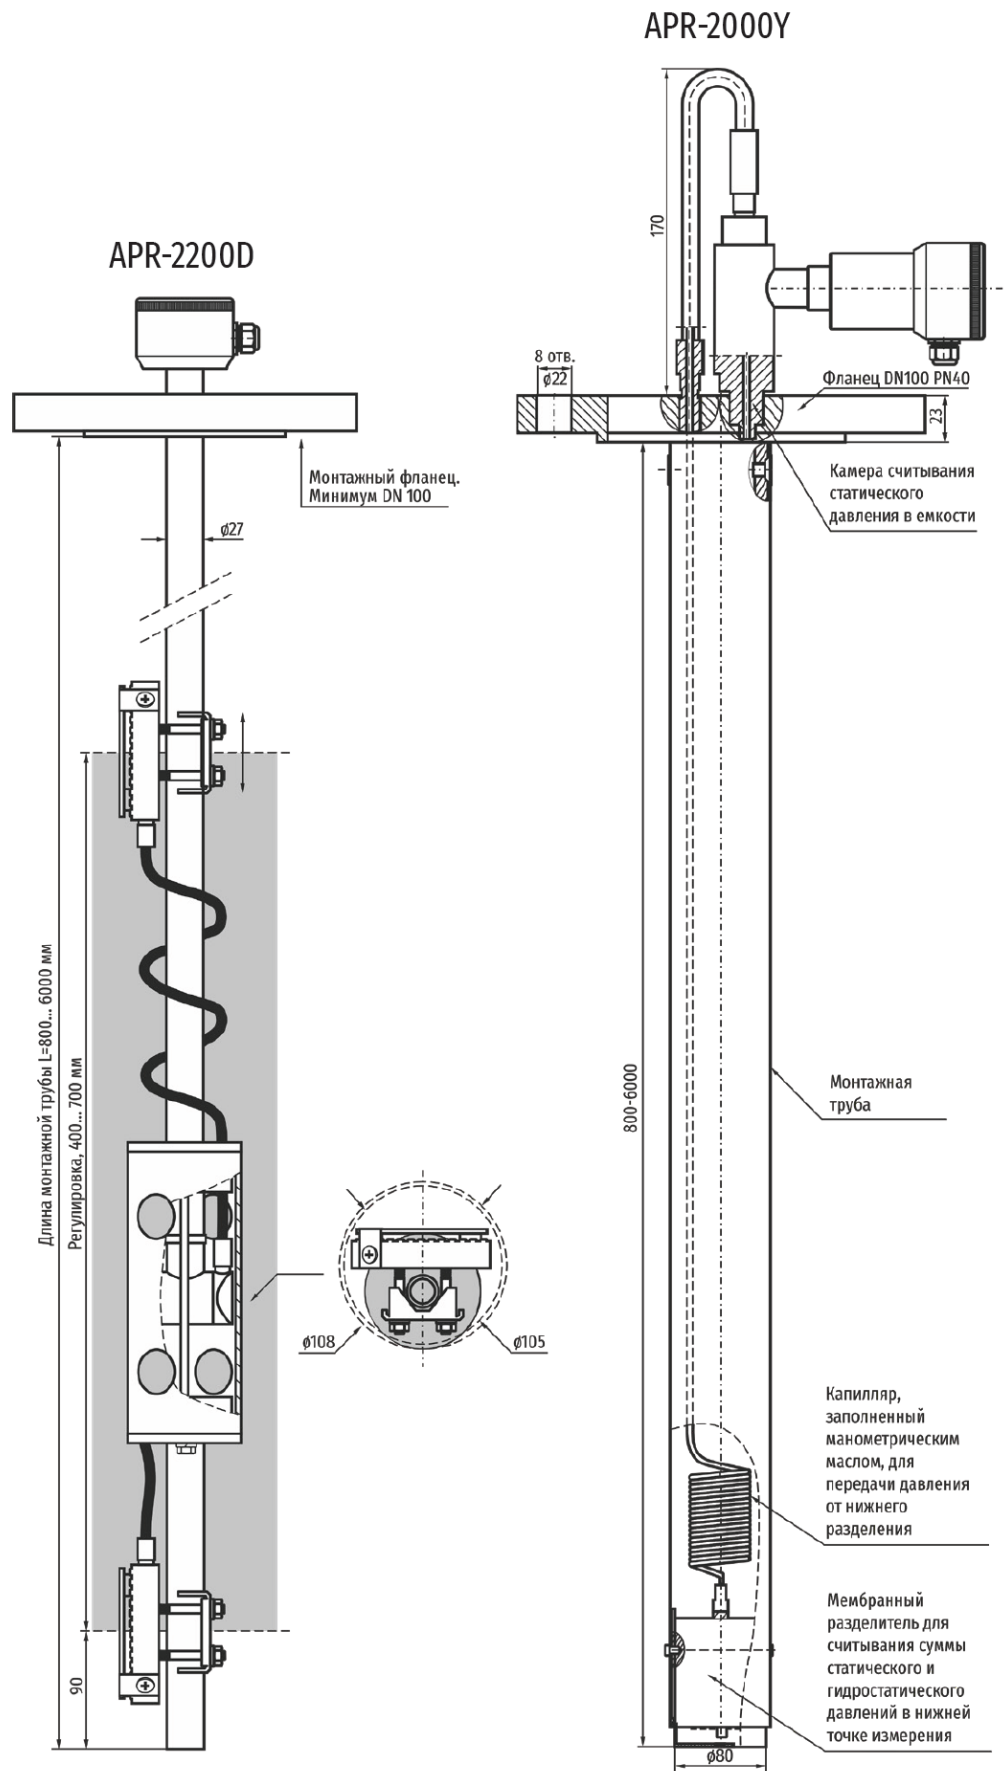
Преобразователи давления измерительные APR-2200D и APR-2000Y. Внешний вид и габаритные размеры
